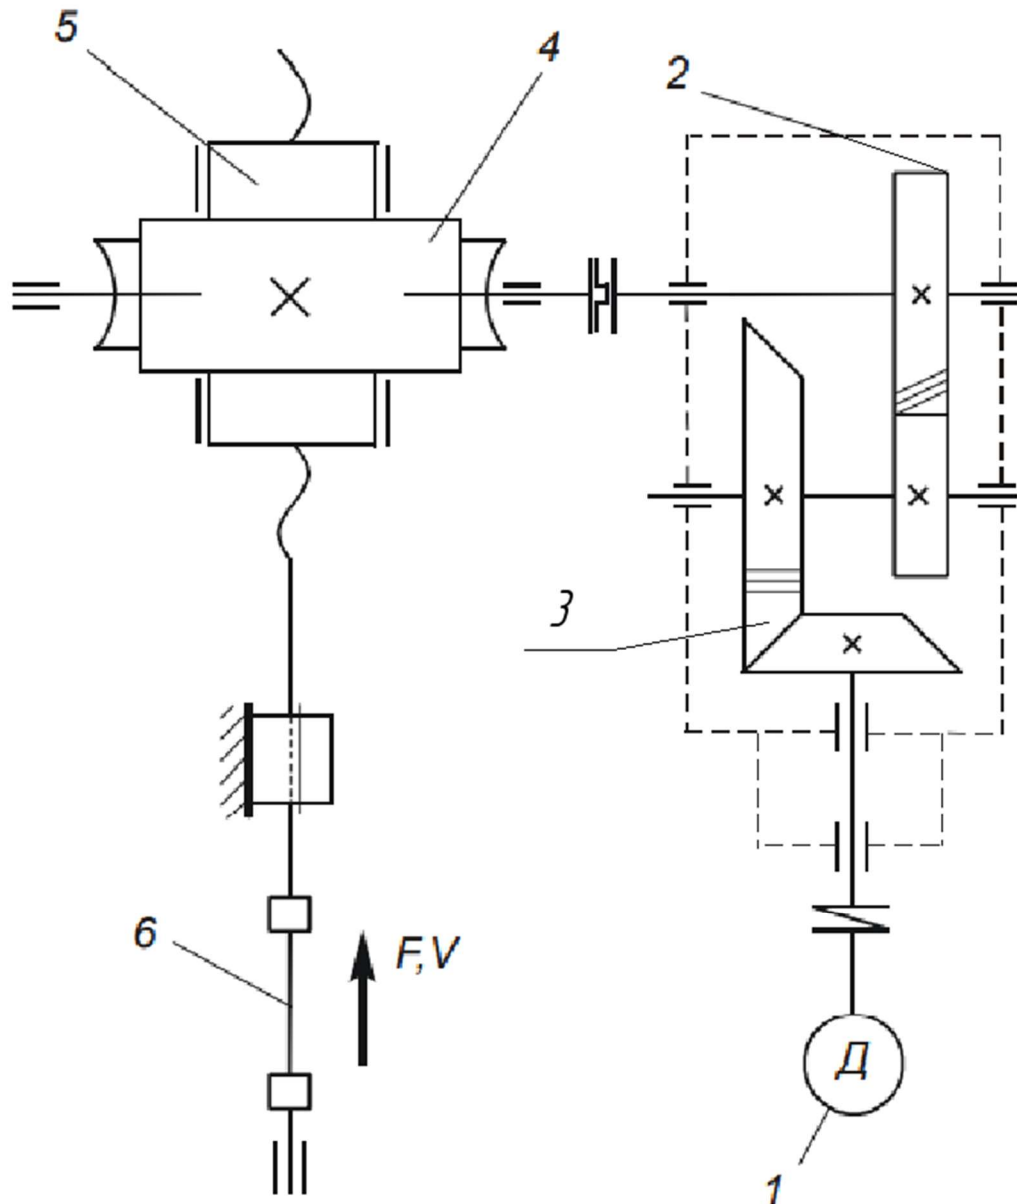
Кінематична схема привода: 1- двигун, 2 – циліндрична косозуба передача; 3 – конічна передача; 4 – черв’ячна передача; 5 – гвинт; 6 – зразок.
